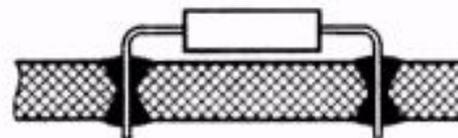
Установка и пайка ЭРИ с плоскими планарными выводами, формованные для установки в сквозное круглое монтажное отверстие
